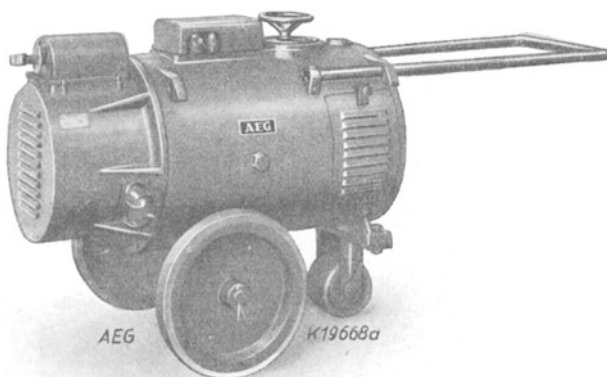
Fahrbarer Eingehäuseumformer mit Querfelddynamo.
